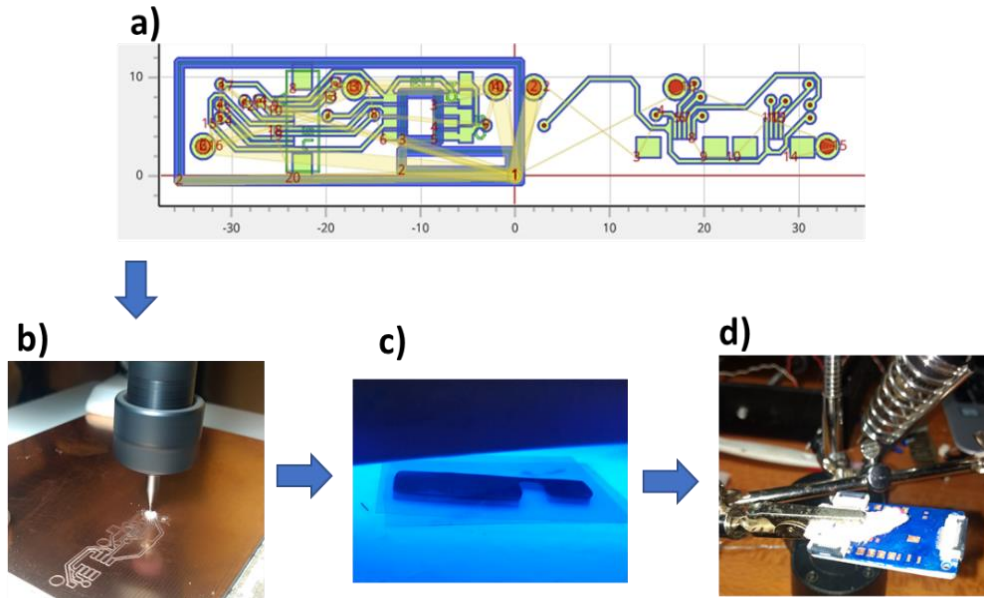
Proceso de manufactura de los circuitos del arreglo instrumental, a) diseño del circuito, b) Manufactura en la *CNC*, c) aplicación de protector curable *UV*, d) soldadura de componentes.
